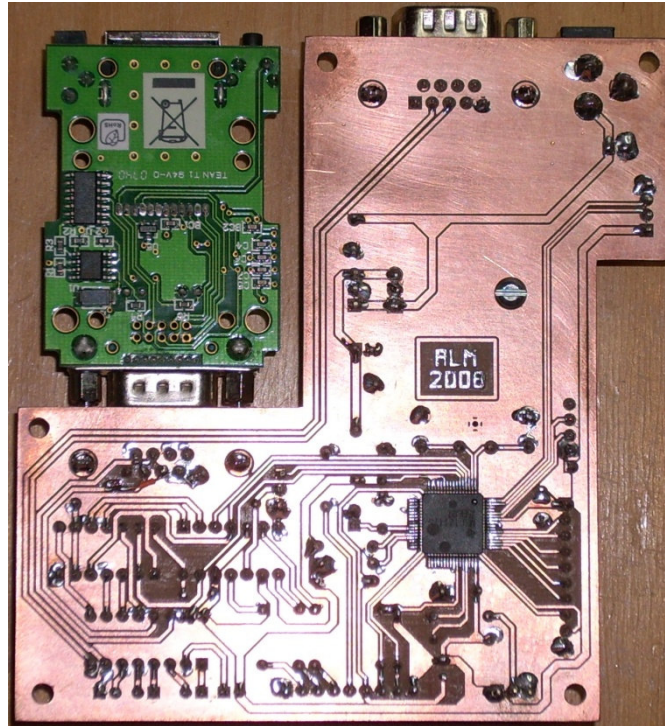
Face inferior da PCB do Módulo Cadastramento montado com o Conversor Tibbo
